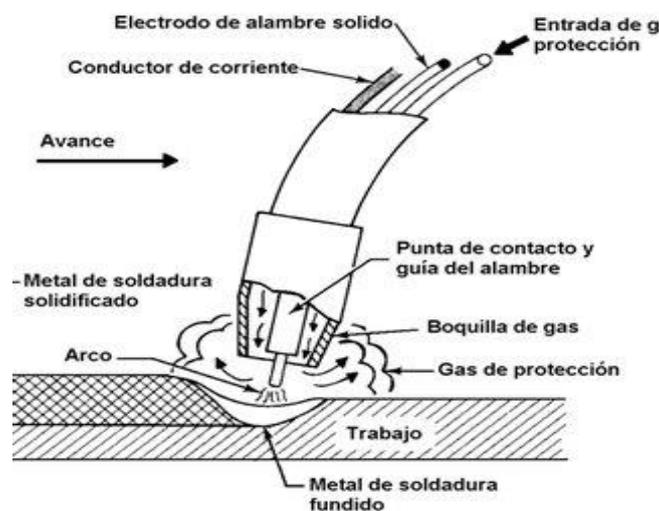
Esquema proceso de soldadura GMAW.
